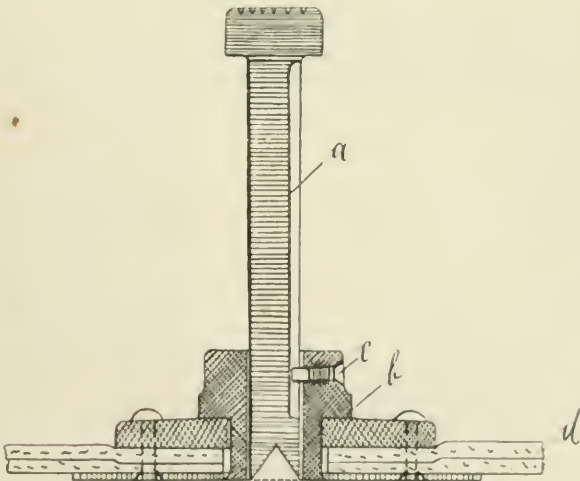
Senkrechter Durchschnitt durch das Mittelstück einer Rinderschlachtmaske. (Nach Kögler.) a Führungsrinne im Schlagbolzen, b eisernes Mittelstück, c Führungsschraube für den Schlagbolzen, d Lederwerk der Maske.
